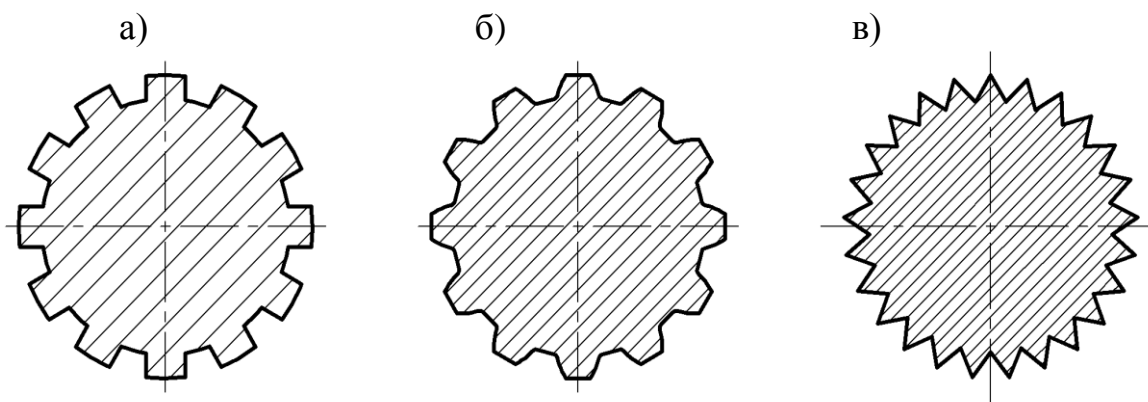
Поперечные сечения шлицевых поверхностей валов: а – прямоугольный профиль; б – эвольвентный профиль; в – треугольный профиль
